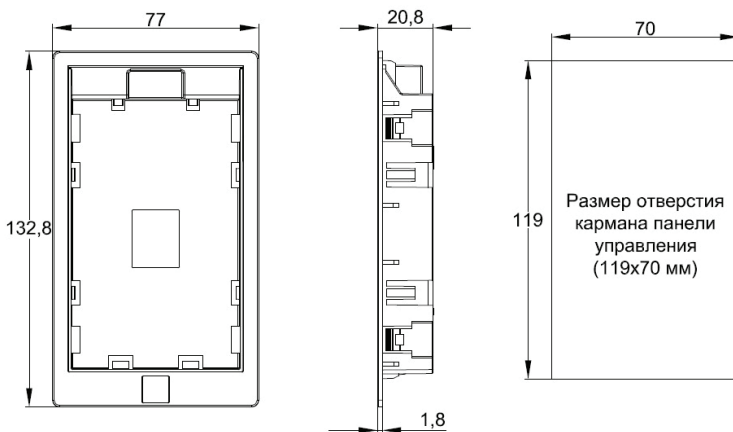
Габаритные размеры держателя внешней цифровой двухстрочной панели управления (единица измерения - мм)
